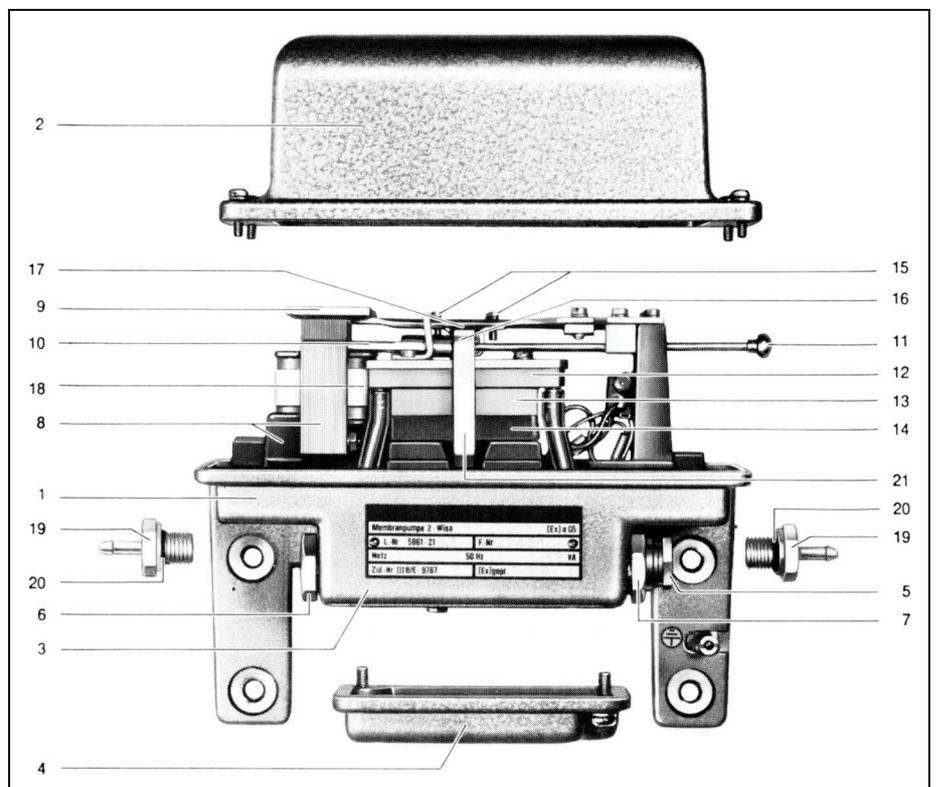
Membranpumpe 2-Ex, Gehäusekappe abgenommen (explosions- und korrosionsgeschützte Ausführung)
